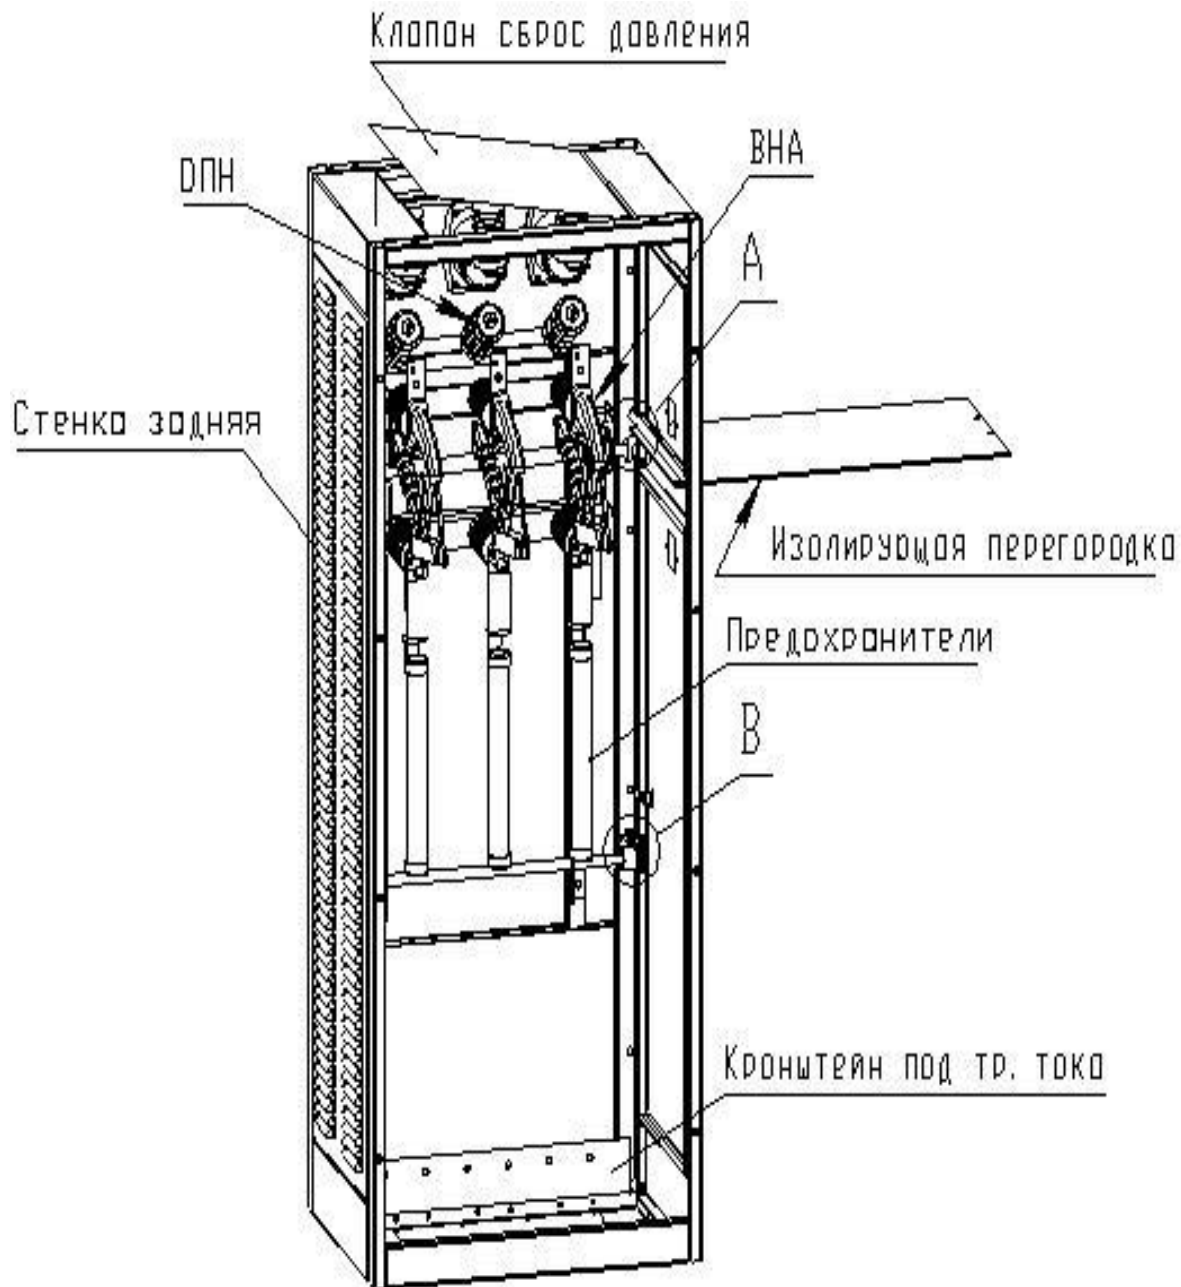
Общий вид камеры серии КСО-303 типоразмера 05
